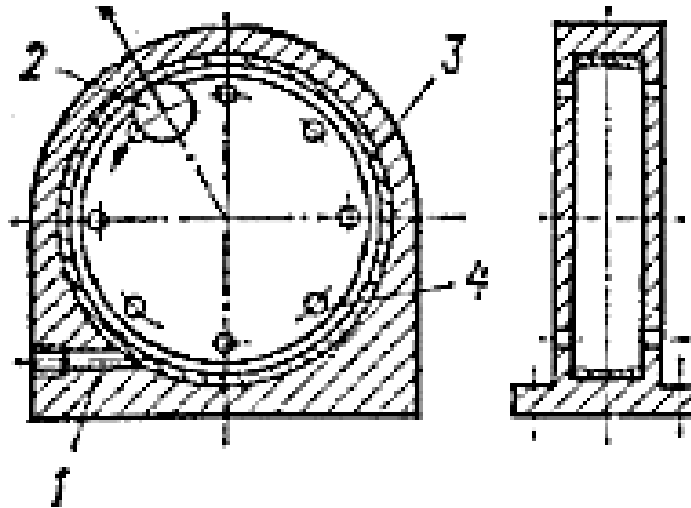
Кульковий пневматичний вібровозбуджувач: 1 - сопло; 2 - кулька; 3 - кільцева доріжка; 4 - отвір для випуску повітря
